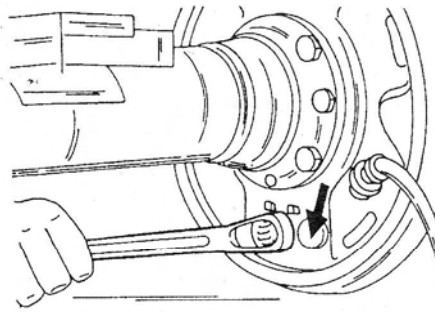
Болт крепит регулировочный механизм Perrot на плате тормозного щита. Рядом (стрелка) расположена пробка регулировочного отверстия.
